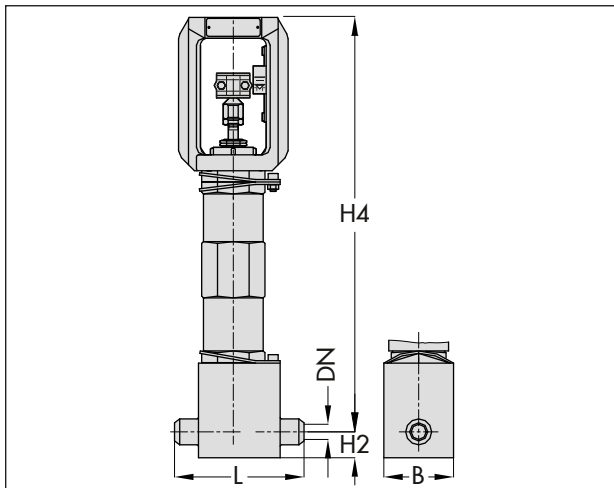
Eckventil Typ 3252 mit Anschweißenden
